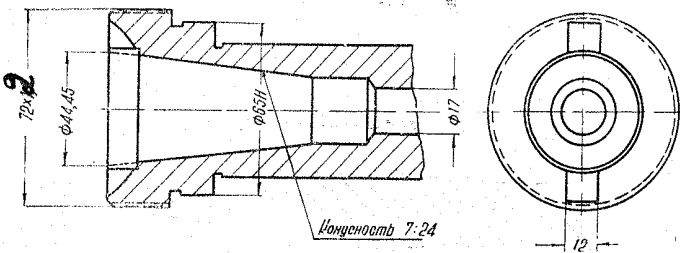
Эскиз конца шпинделя поворотной головки станка модели 6М82Ш
